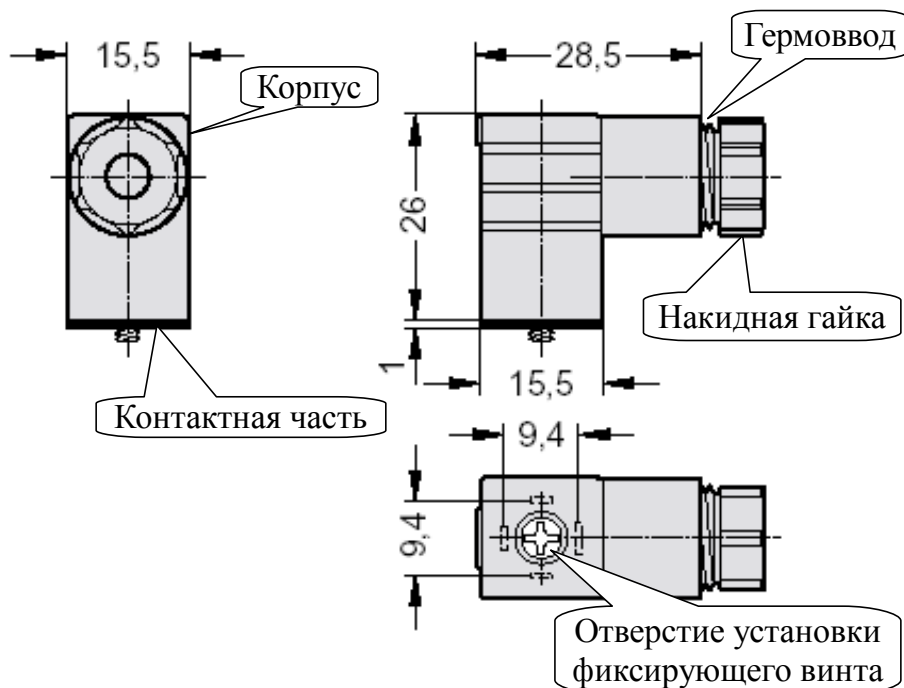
Герморазъём DIN 43650, форма С (соединитель электрический, промышленный стандарт) с тремя контактами плюс заземляющий контакт
